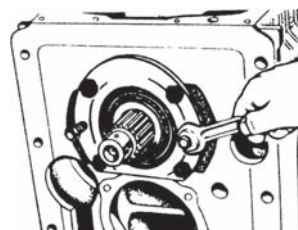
Спрессовка стакана подшипника вторичного вала. Снятие вторичного вала, замена ведомой шестерни II ступени редуктора.
